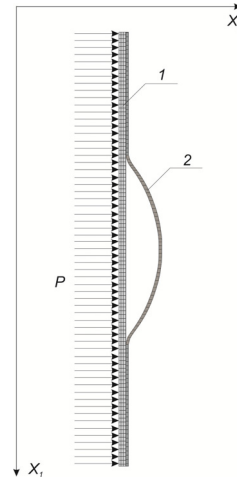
Исходная 2D-конечно-элементная модель заготовки трубы и матрицы: 1 – заготовка; 2 – матрица
